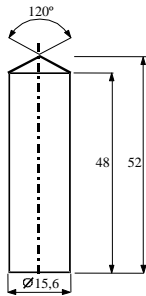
Piston cylindrique en bronze, dimensions en mm
